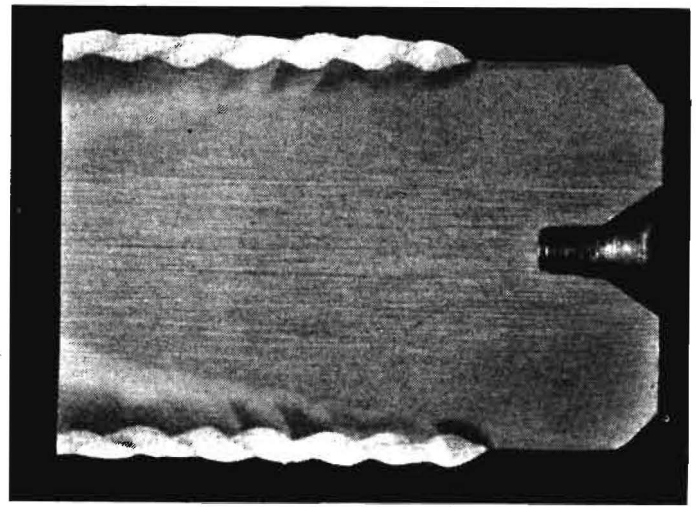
Makroschliff (Längsschnitt) vom aufgeschweißten Bauteil
